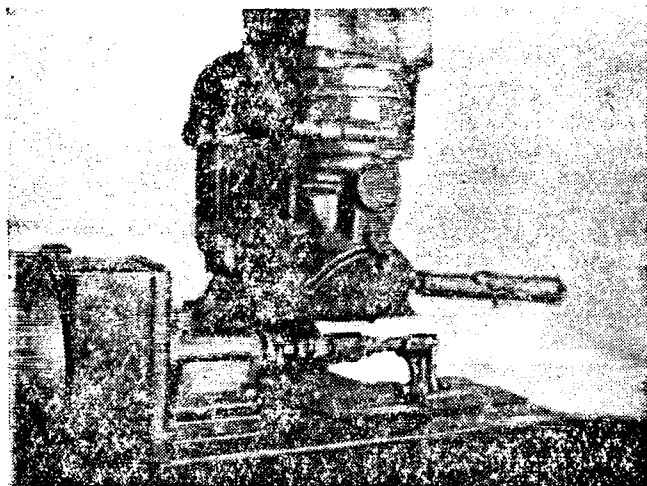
Заточка червячной фрезы на станке Барбер-Кольман
